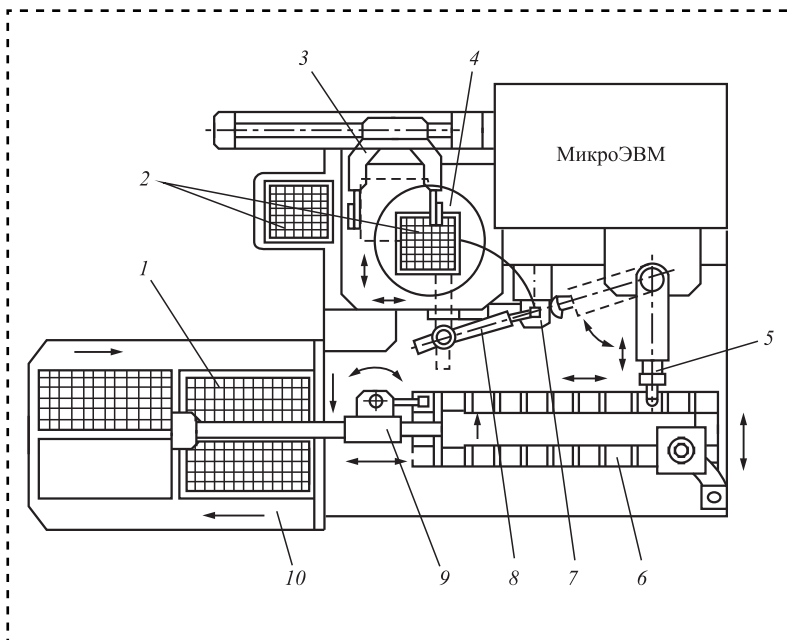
Схема автомата установки полупроводникового кристалла в корпус ИМС:
